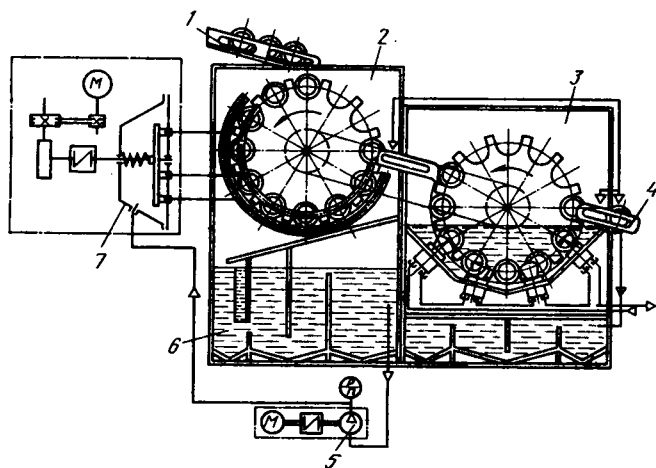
Схема роторной линии РЛКП-100 для промывки колец
